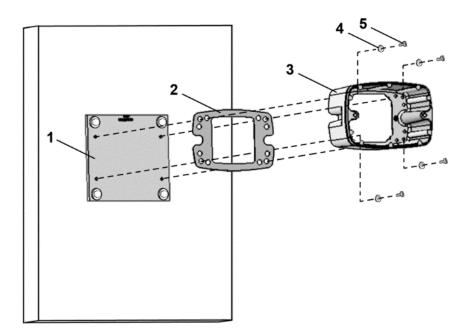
Befestigung des Becher BG. D an der Adapterplatte
